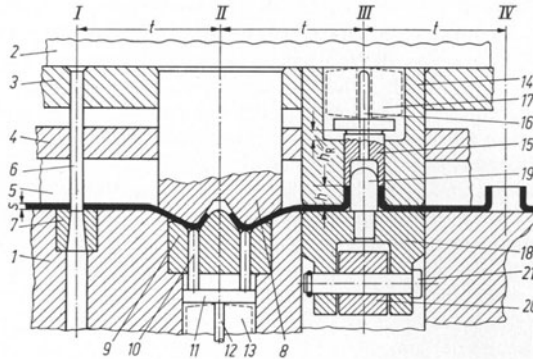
Verbundfolgewerkzeug zur Erzeugung hoher Kragens für Gewinde
